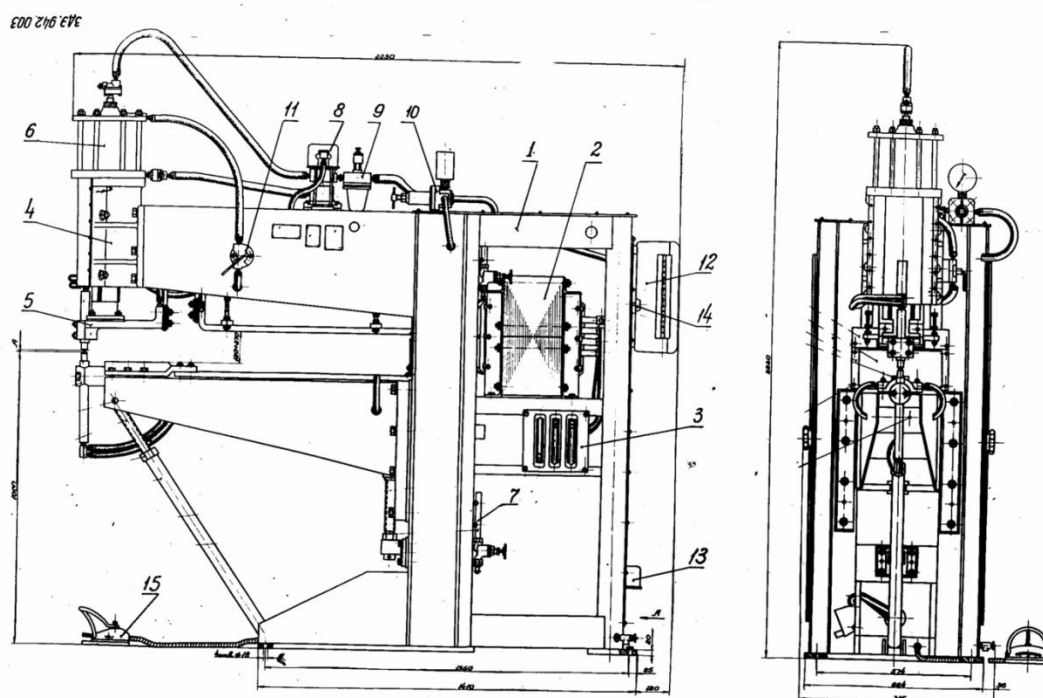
Конструкция машины для контактной сварки МТПУ-300
